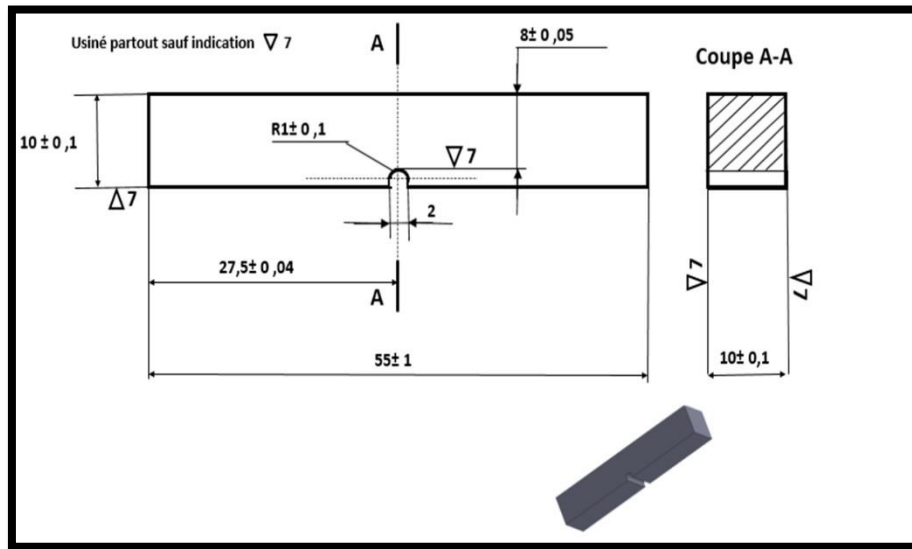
Dimensions standard de l'éprouvette de résilience (Charpy U).
